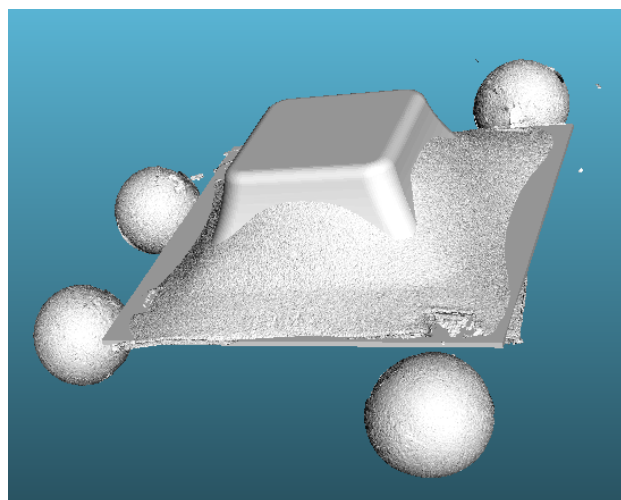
Superposició de la peça teòrica amb la peça fabricada
